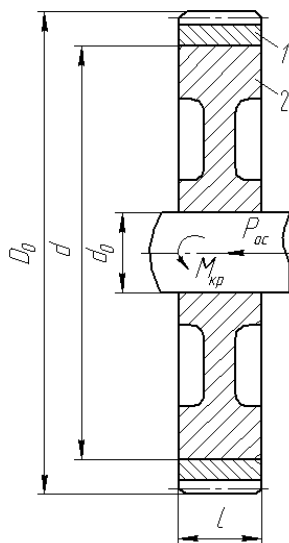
Схема запрессовки зубчатого венца (1) косозубого колеса на ступицу (2)
